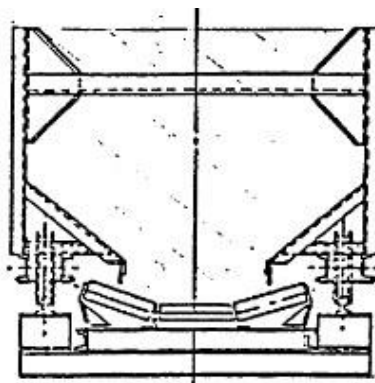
Plan przenośnika bunkrowego [86]
